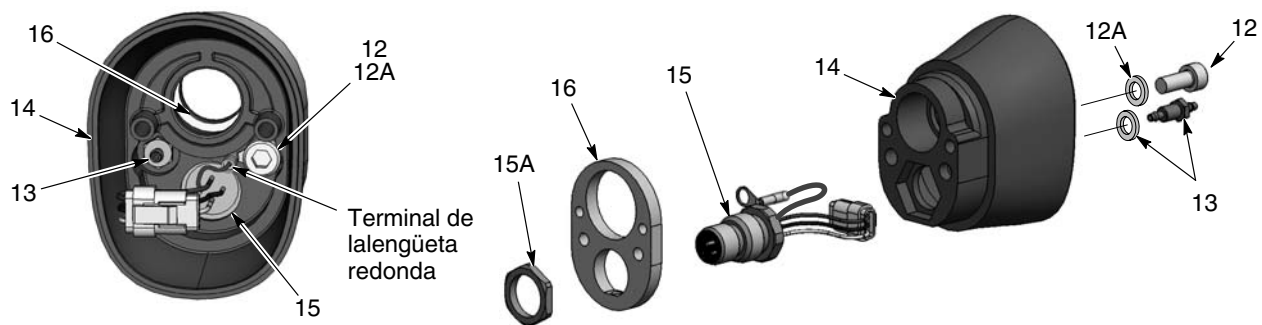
Desmontaje de la pistola de montaje en tubo 5 de 5
